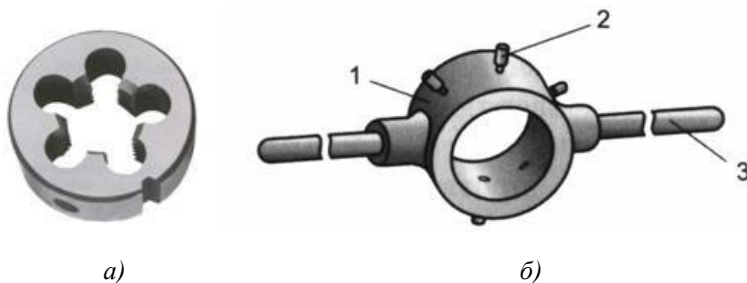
Приспособления для нарезания наружной резьбы: а – круглая цельная плашка; б – вороток для плашки (плашкодержатель)
